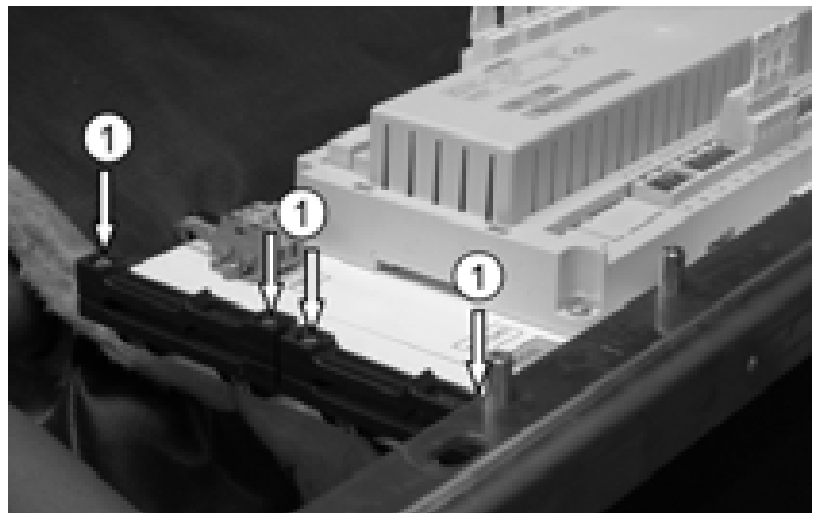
Zugentlastungen mit je zwei Kreuzschlitzschrauben ①
